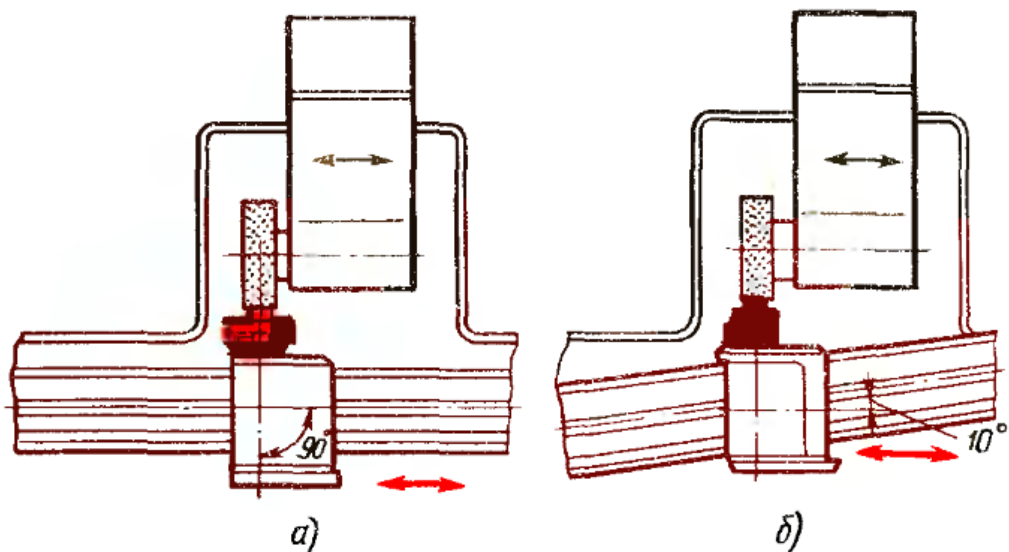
Схема наладки станка для шлифования плоских поверхностей фланцев: а — низко, б — высоко
